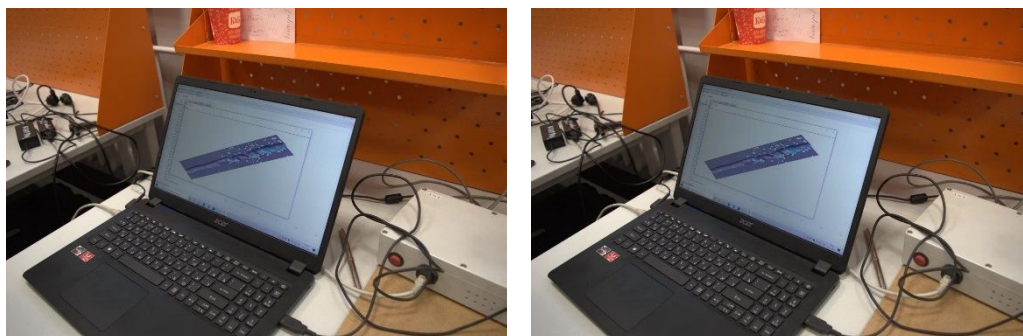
Цифровая оценка качества выполненного сварного шва по технологии 3DLD
